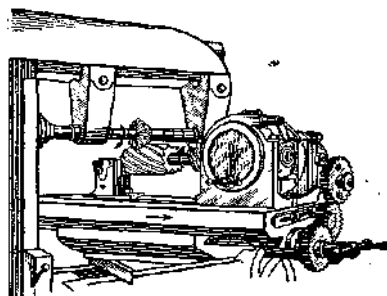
Фрезерування спіральної канавки на універсально-фрезерному верстаті
